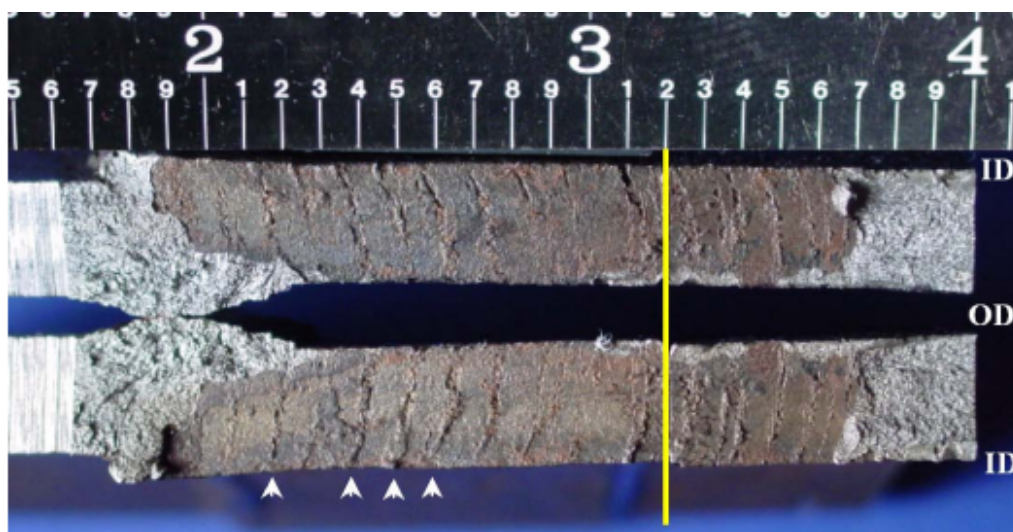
Patrón de *stitching* en superficie de fractura de soldadura ERW.
